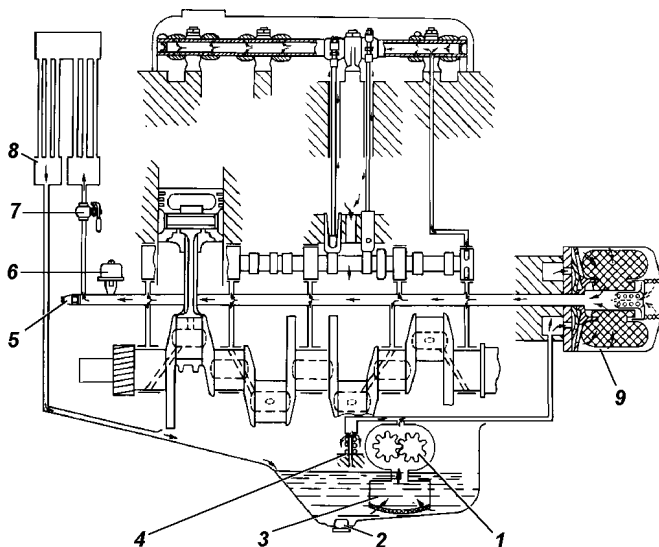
Схема системы смазки двигателей УМЗ:
